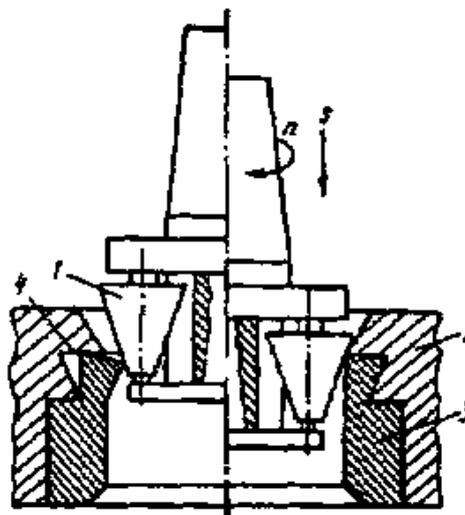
Схема сборки клапанного седла вальцеванием
